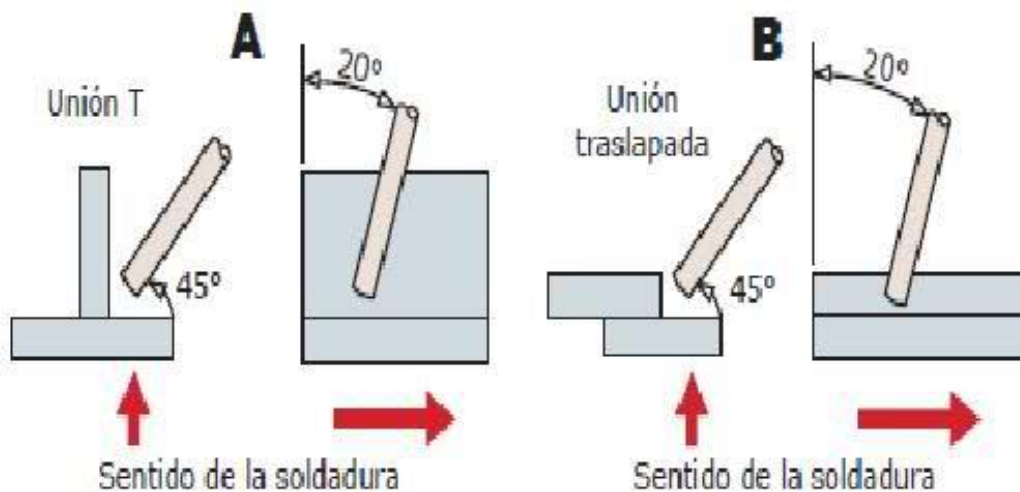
Angulos de los electrodos para soldadura de filete
